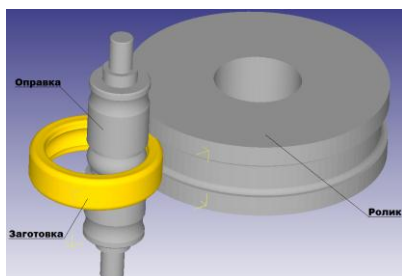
Расчётная модель процесса раскатки кольца подшипника
